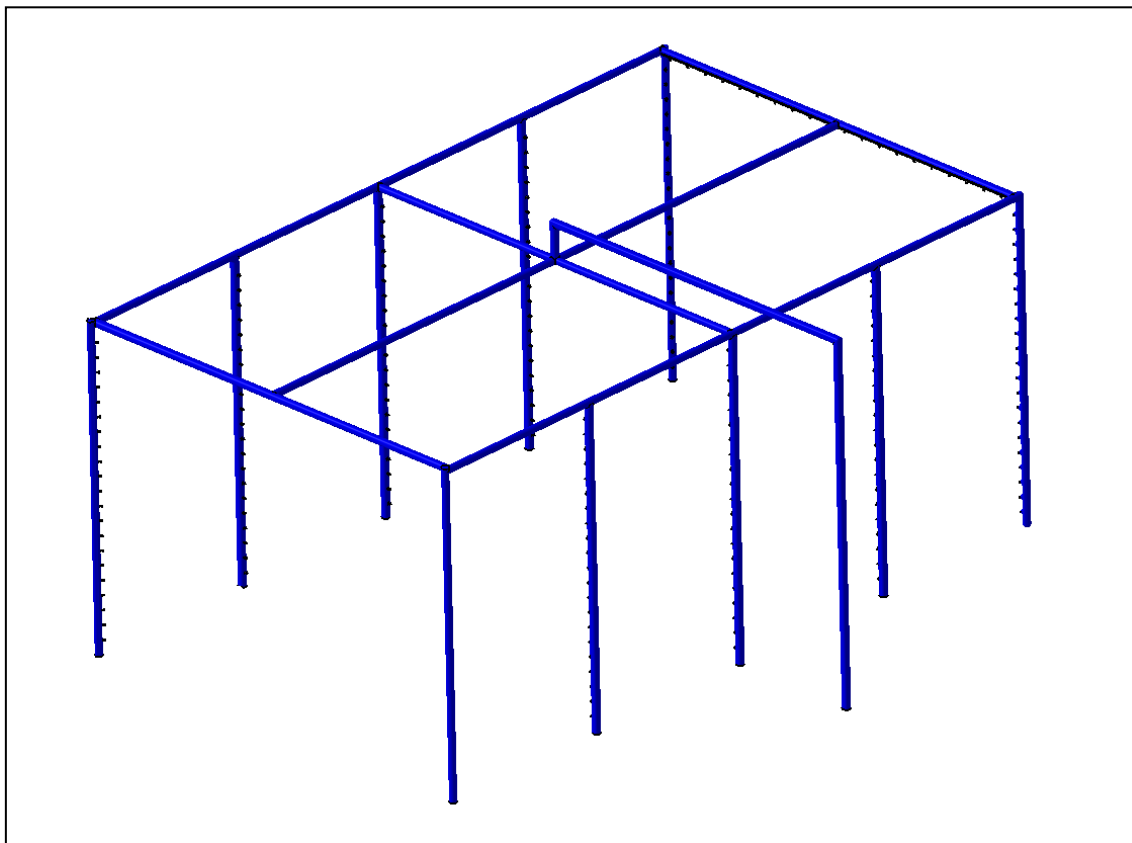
Estructura de tuberías y boquillas de la cabina de lavado.
